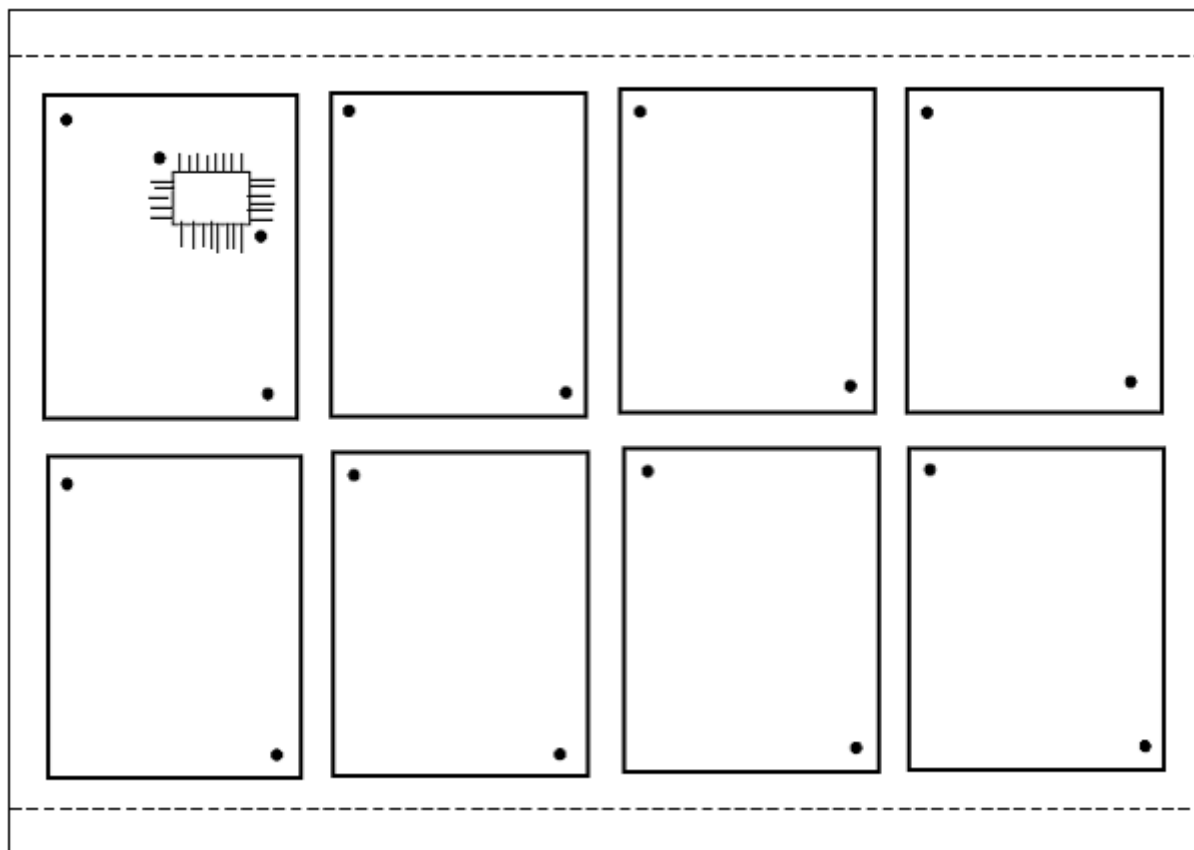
Пример расположения нескольких плат на одной заготовке.
